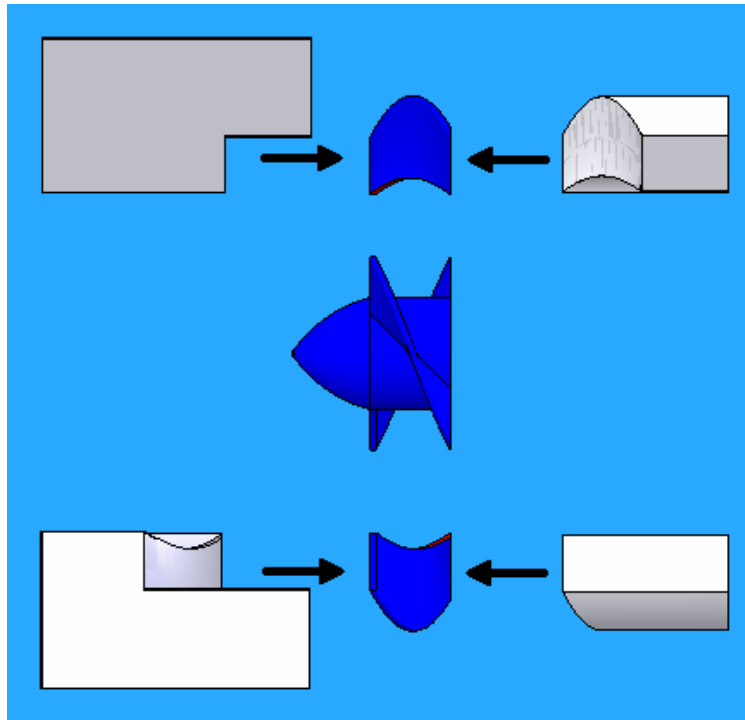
Sujeción de dos álabes, previo a la soldadura, parte I.
